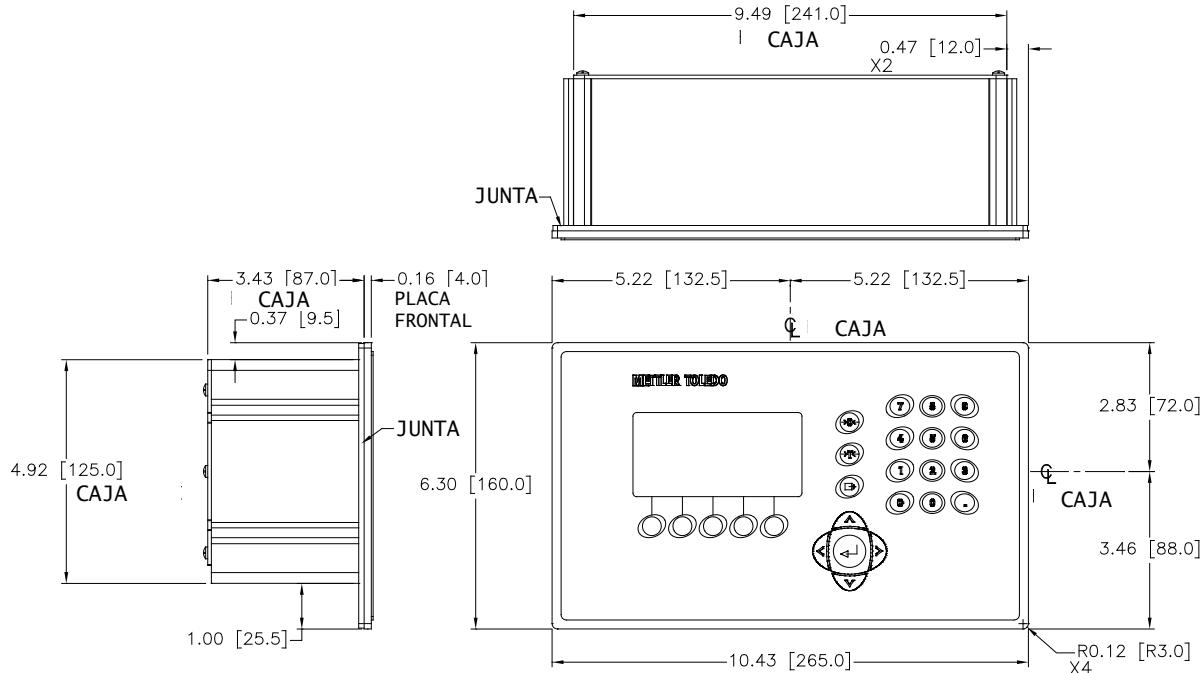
Dimensiones de la caja tipo montaje en panel del IND560
